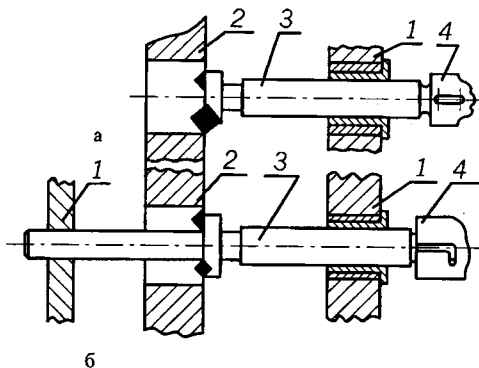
Схеми розточки отворів: а — односторонній напрям розточної оправки; б - двосторонній напрям розточної оправки; 1 - кондукторна плита; 2 - заготовка; 3 - оправка з різцьовою головкою; 4 - шпindelь верстата.
